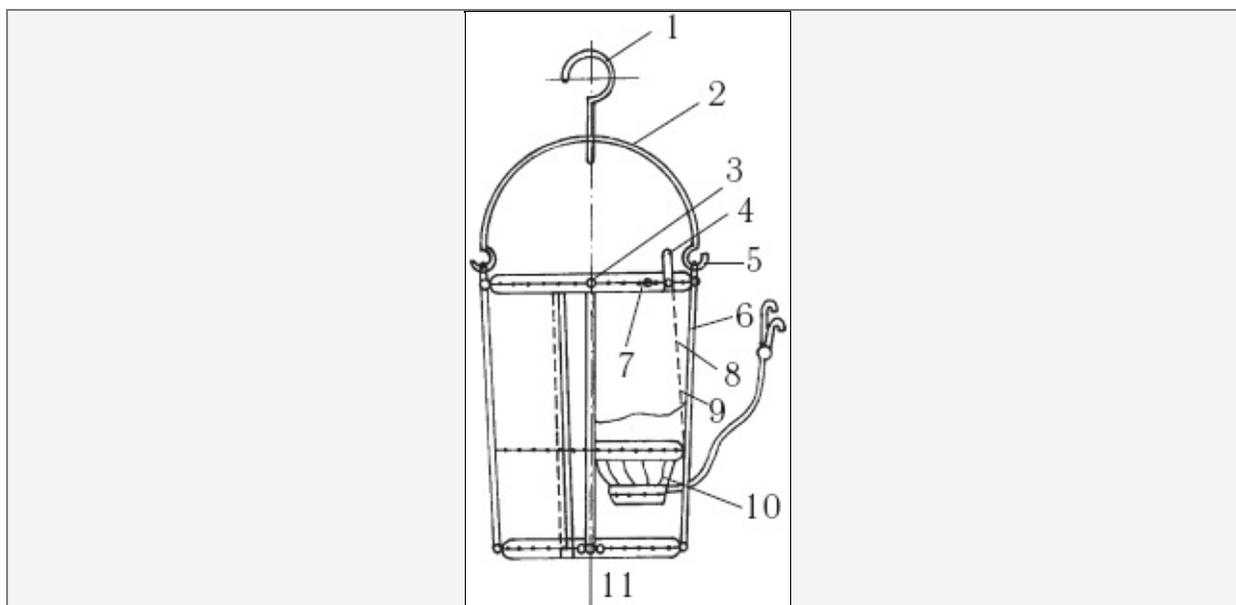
Плодосборная сумка: 1 – подвеска; 2 – дужка; 3 – стойка; 4 – крючок; 5 – крючок дужки; 6 – стойка с ушком; 7 и 11 – верхнее и нижнее кольца; 8 – конический корпус; 9 – стягивающий шнур; 10 – самораскрывающееся дно
